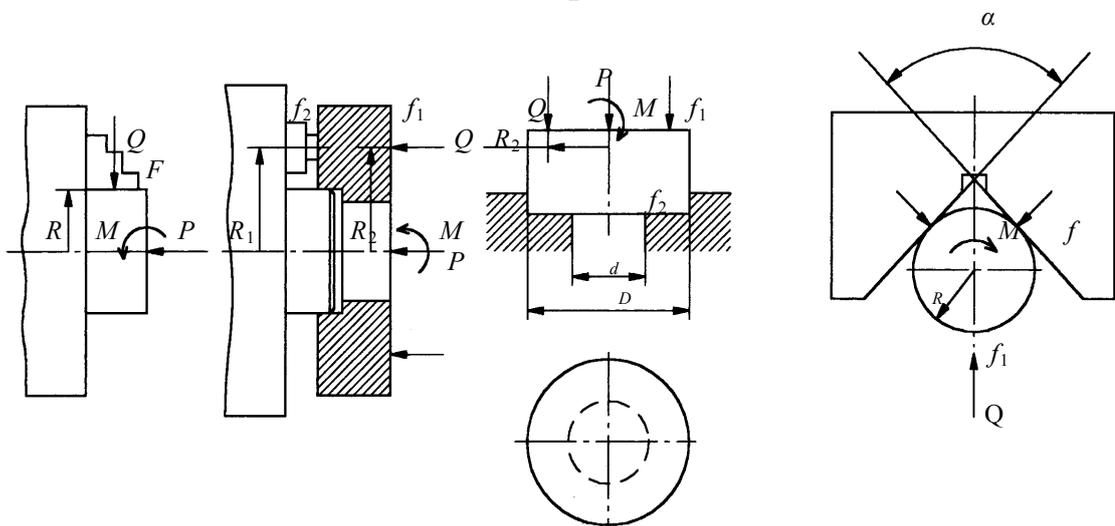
Схемы для расчета сил закрепления заготовки от проворачивания
